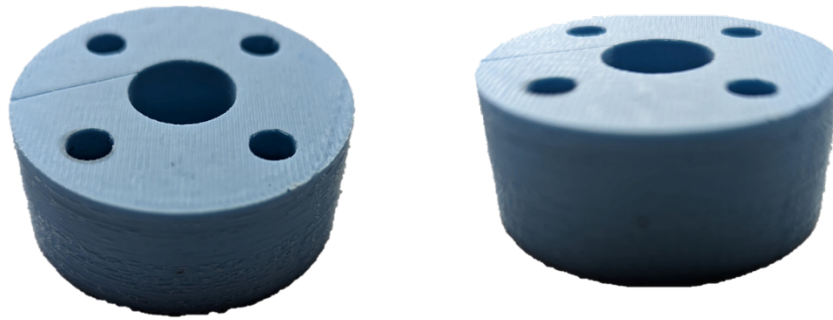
Postać konstrukcyjna pierwszego opracowanego rozwiązania
